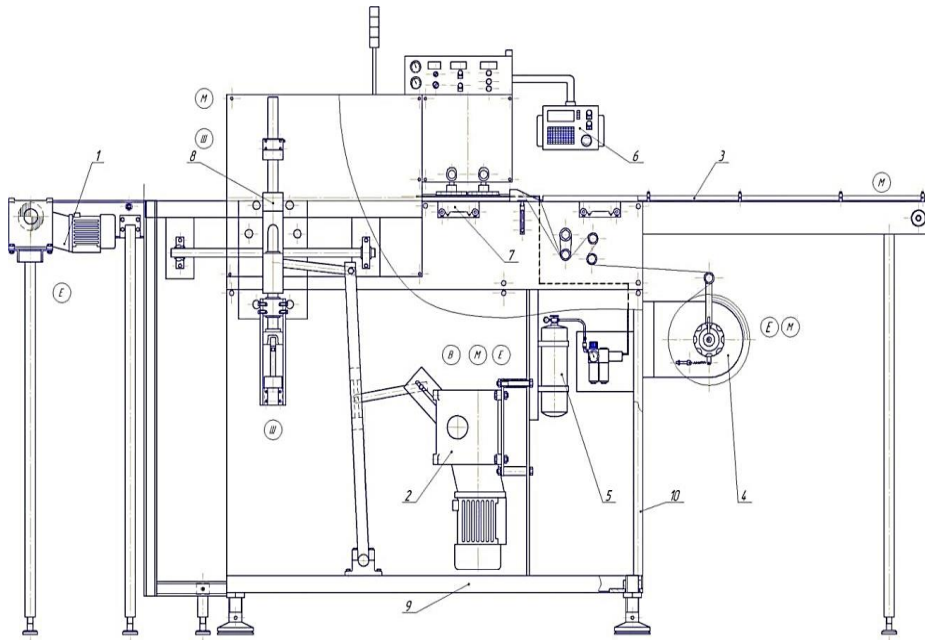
Конструкція горизонтального пакувального автомату Servo 500 Linux Zani : 1- привід стрічкового конвеєра; 2- привід механізму поперечного зварювання; 3 - стрічковий конвеєр; 4 - тримач рулону; 5 - пневматичний блок; 6 - панель керування; 7 - модуль поздовжнього зварювання; 8 - модуль поперечного зварювання; 9 - каркас (рама); 10 - опорна конструкція.
